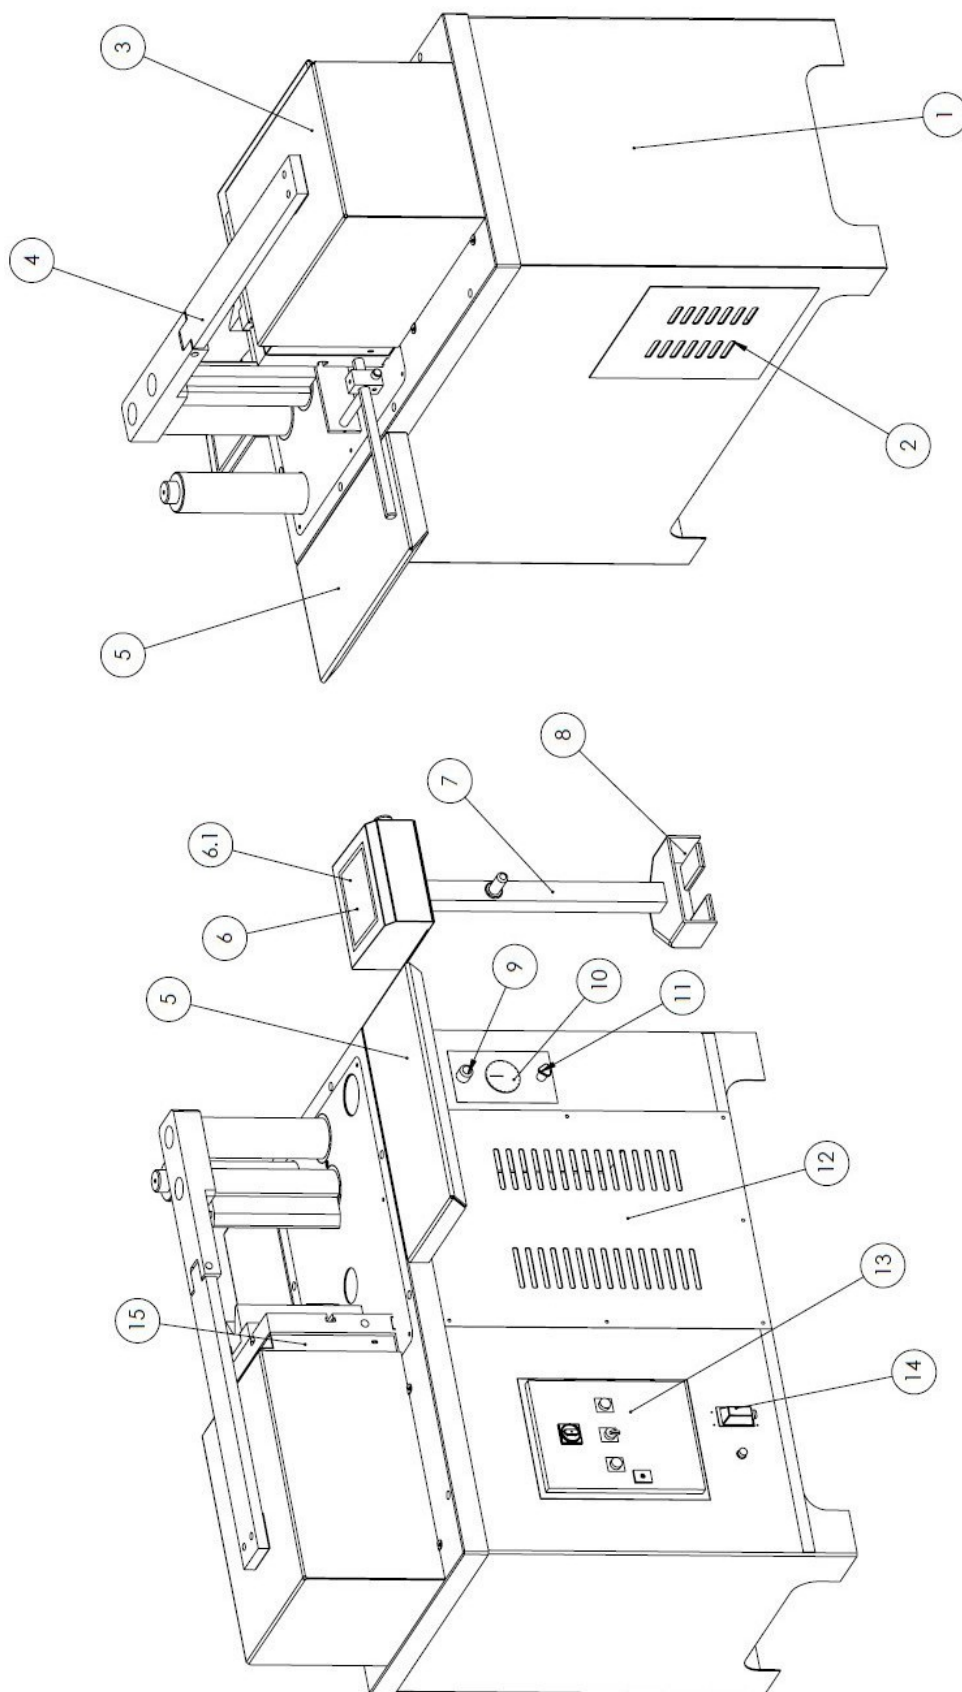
Dessin des pièces 1 Machine complète HBP 30
